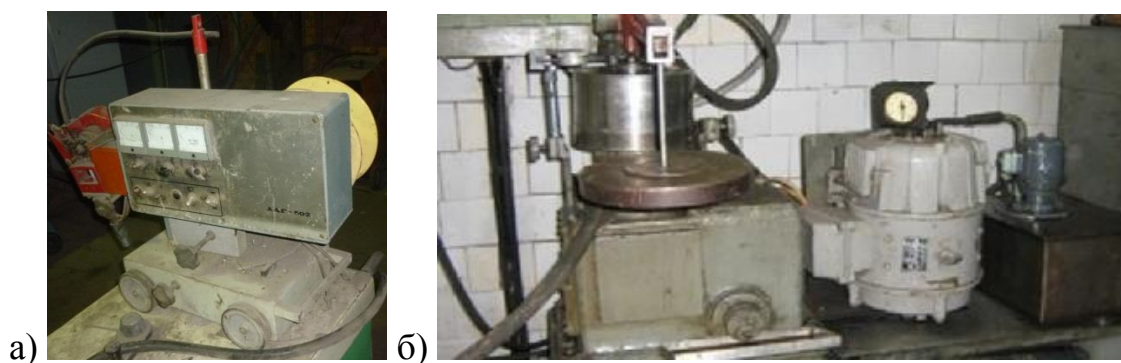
Оборудование для проведения испытаний: автомат для сварки и наплавки в среде защитных газов АДГ-502 (а) и стенд для испытания на истирание (б)
